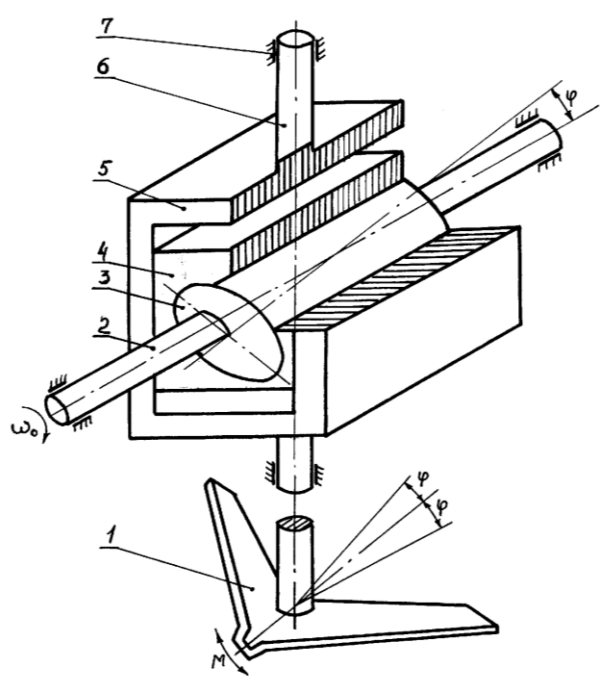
Конструктивна схема плоскоріза з активною лапою і з примусовим автоколиванням 1 – лапа; 2 – ведучій вал; 3 – ексцентрик; 4 – втулка; 5 – корпус; 6 – стояк; 7 – опора.
